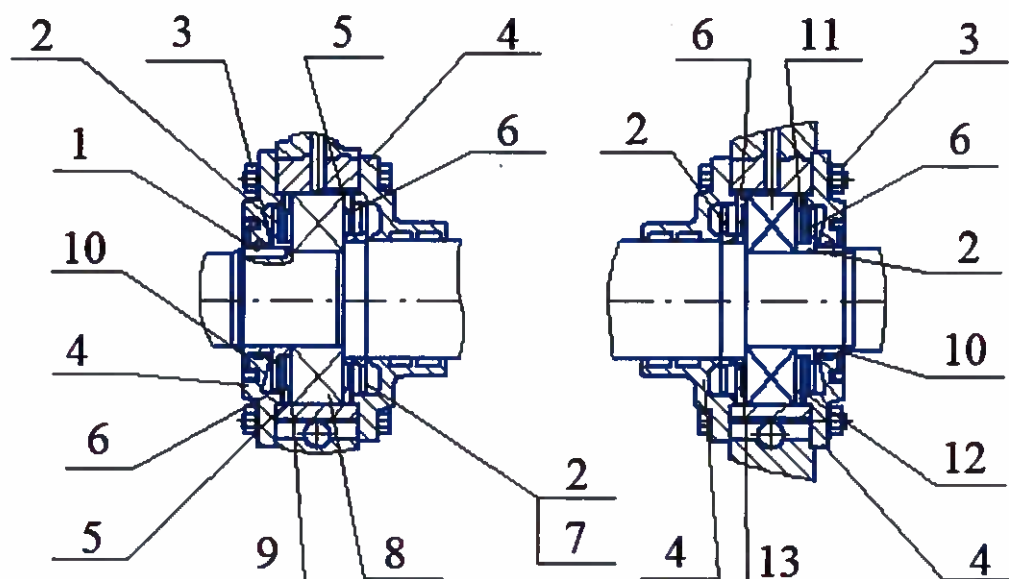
Подшипниковые щиты двигателя рДМ180М2
